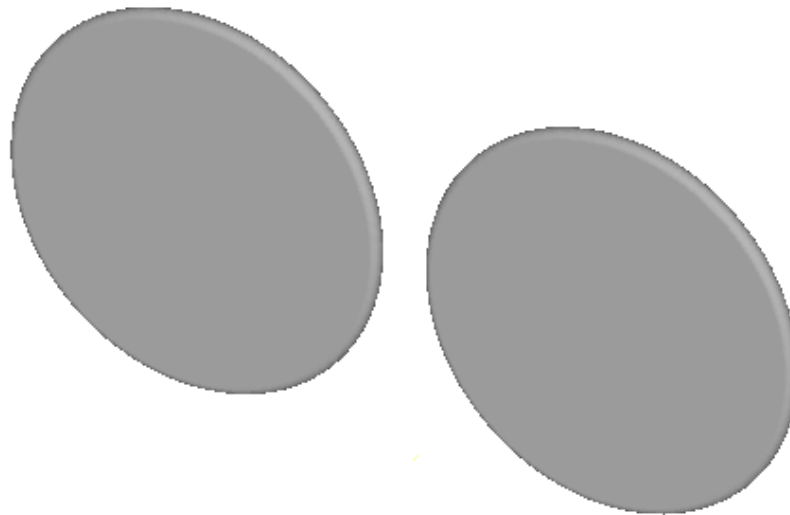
Roletes ou apoio superior e inferior, em SolidWorks 3D, posicionados simetricamente, para serem inseridos no DEFORM 3D™.
